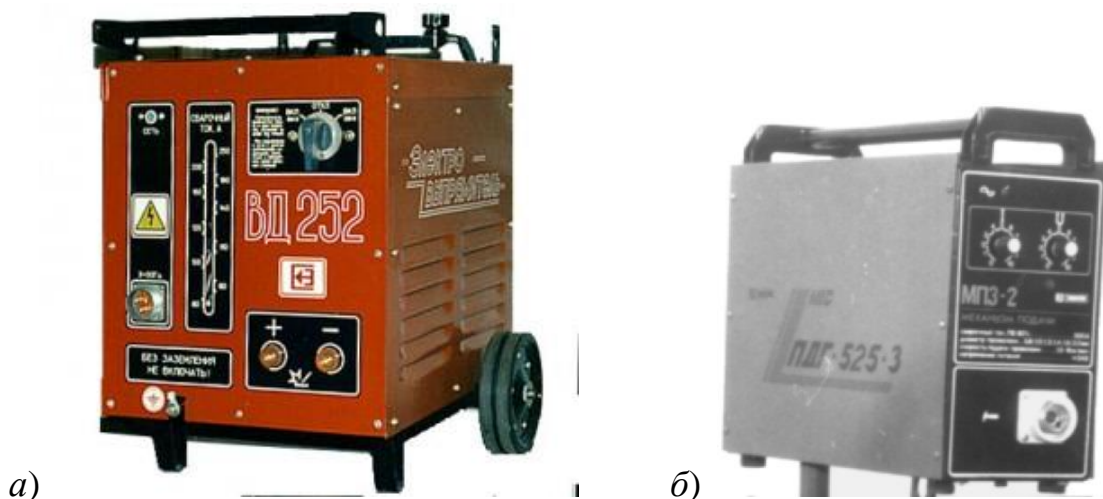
Оборудование для заварки разделанной трещины: сварочный выпрямитель ВД-252 (а) и сварочный полуавтомат ПДГ-525 (б)
